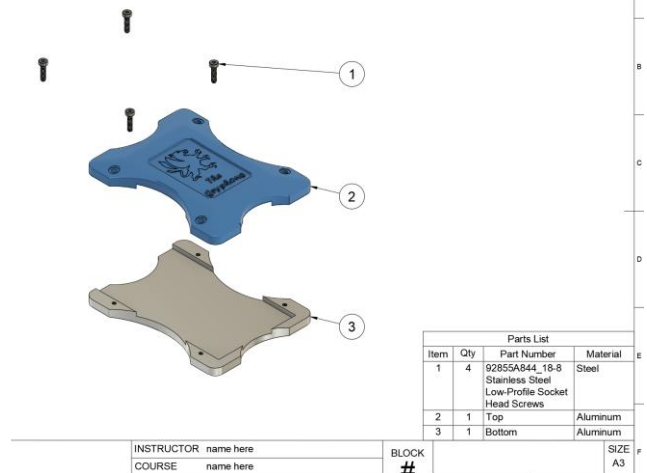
Explosionsansicht mit Teileliste und Positionsnummern
